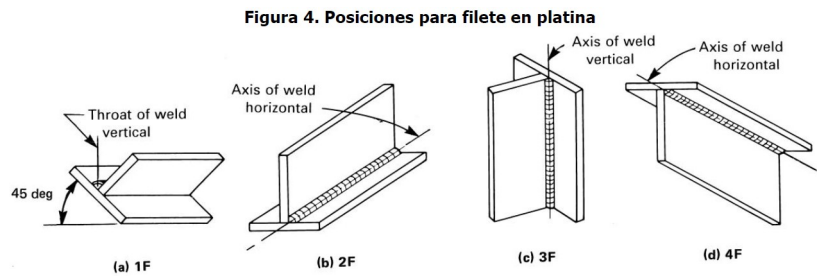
POSICIONES DE PLACAS PARA SOLDADURA DE FILETE.
